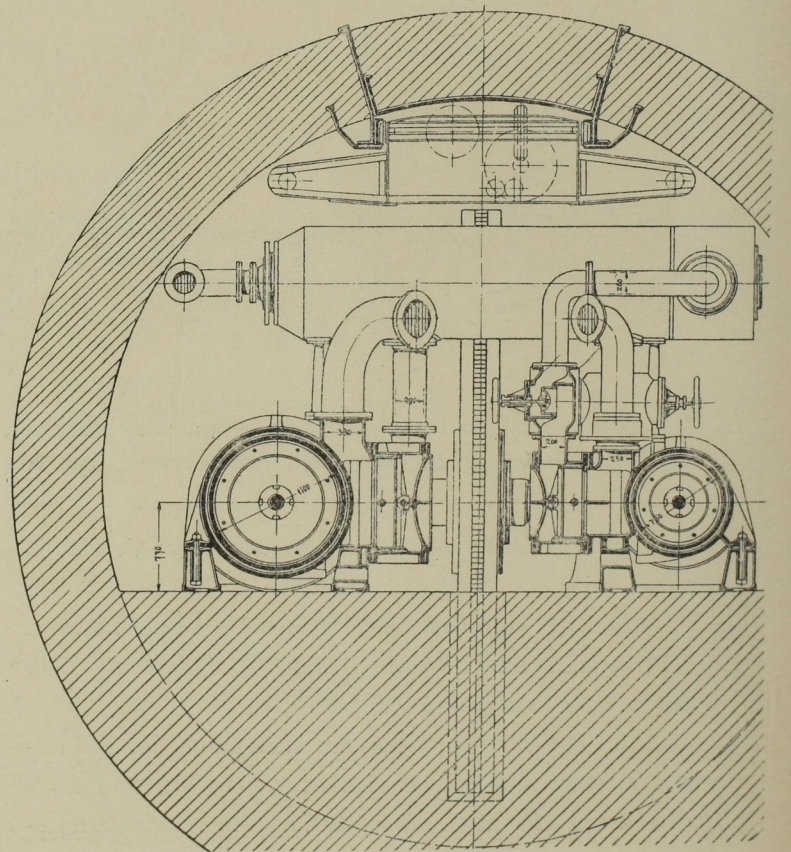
Querschnitt der Maschine. Masst. 1:60.
